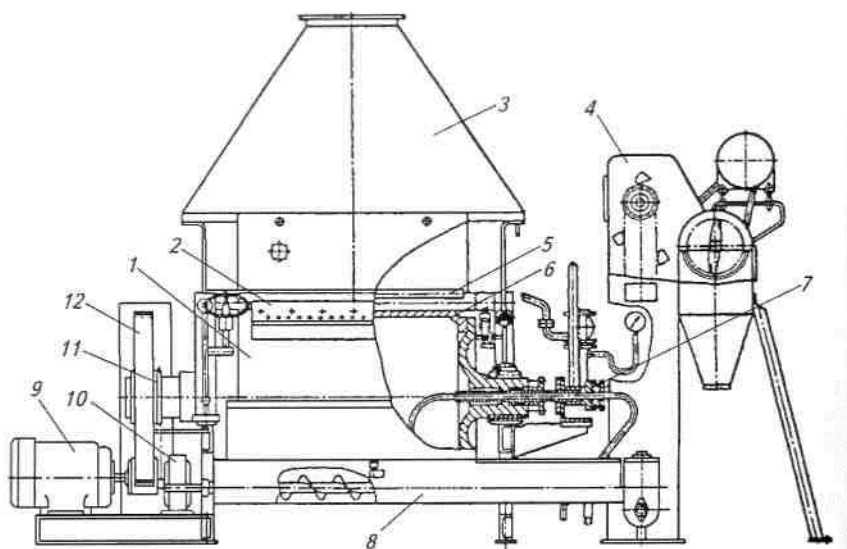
Схема вальцовой сушилки для обезжиренного молока: 1 — сушилка; 2 — ножи; 3 — зонт; 4 — дробилка; 5 — коллекторы; 6 — вальцы; 7 — сальниковое устройство; 8 — шнек; 9 — электродвигатель; 10 — редуктор; 11 — цепная передача; 12 — зубчатые колеса
